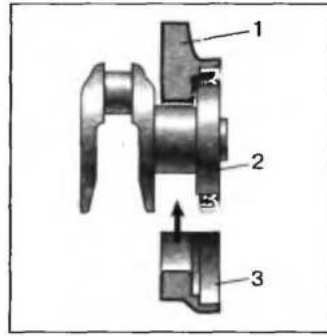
Установка заднего сальника коленчатого вала перед установкой крышки коренного подшипника: 1 — блок цилиндров; 2 — коленчатый вал; 3 — крышка коренного подшипника
